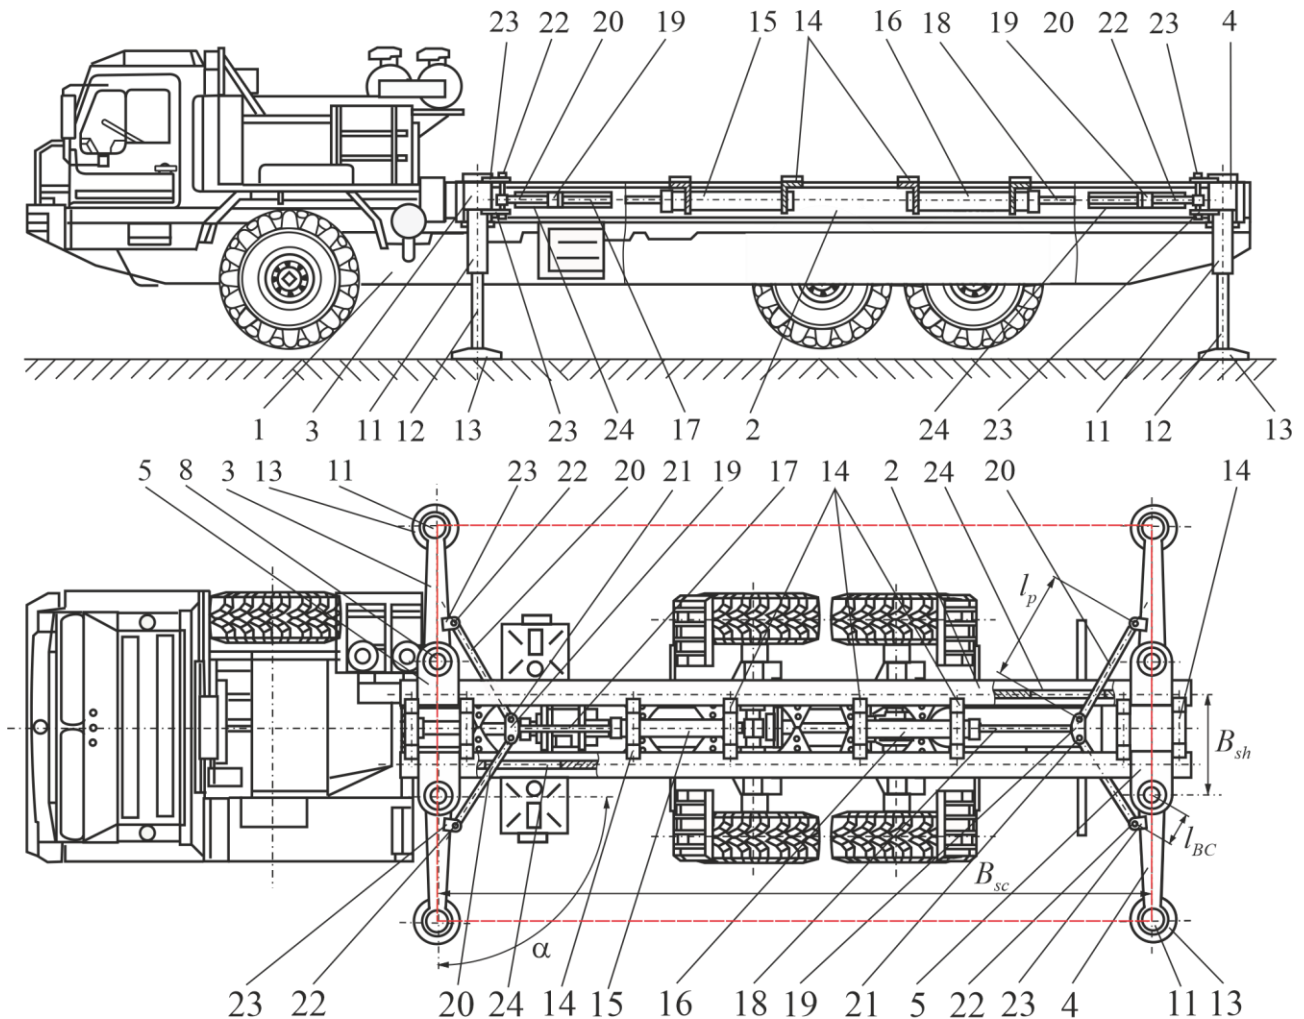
Общий вид транспортно-технологической машины с выносными опорами исследуемой конструкции в рабочем положении [16]
